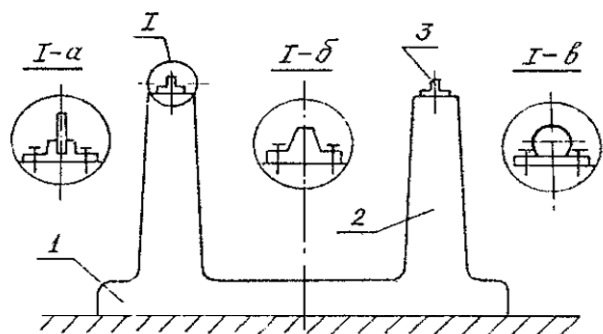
Устройство для статической балансировки роторов на линейных опорах: 1 – основание; 2 – стойка; 3 – линейная опора; нож (I - а); призма (I - б); скалка (I - в)
